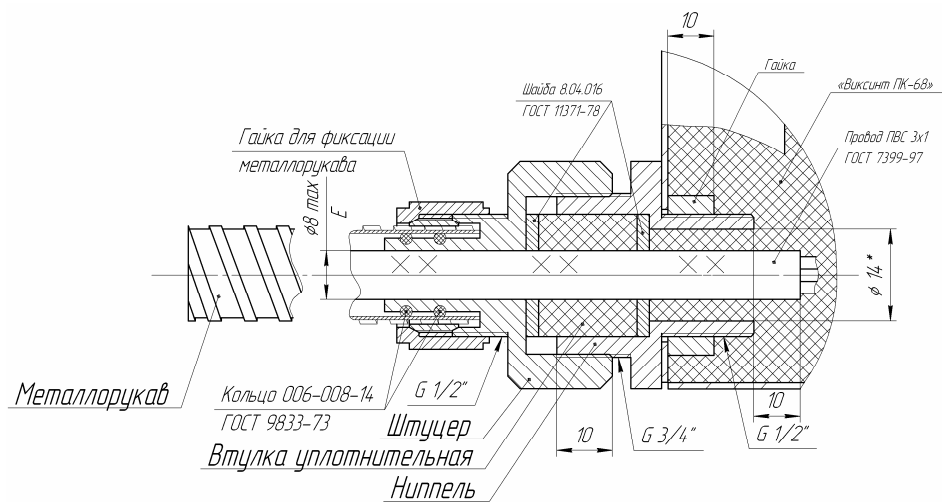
Кабельный ввод с элементами конструкции, обеспечивающими взрывозащиту светозвукового оповещателя «СЗО-Фотон»
